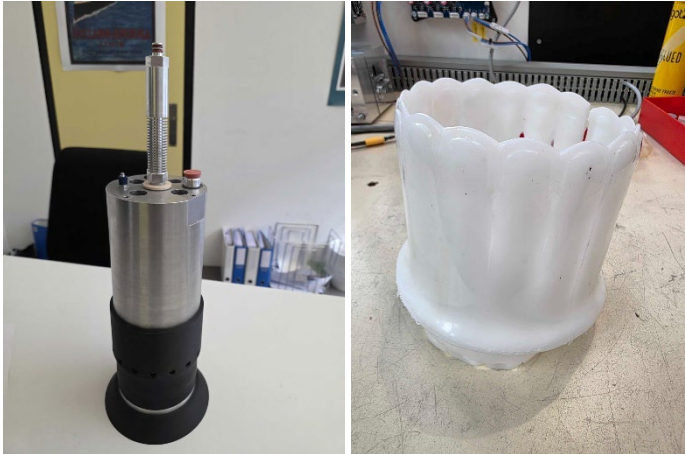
Prototyp 136 mm Variante Extrusionseinheit, extrudiertes Stück Durchmesser 136 mm (v.l.n.r.)
